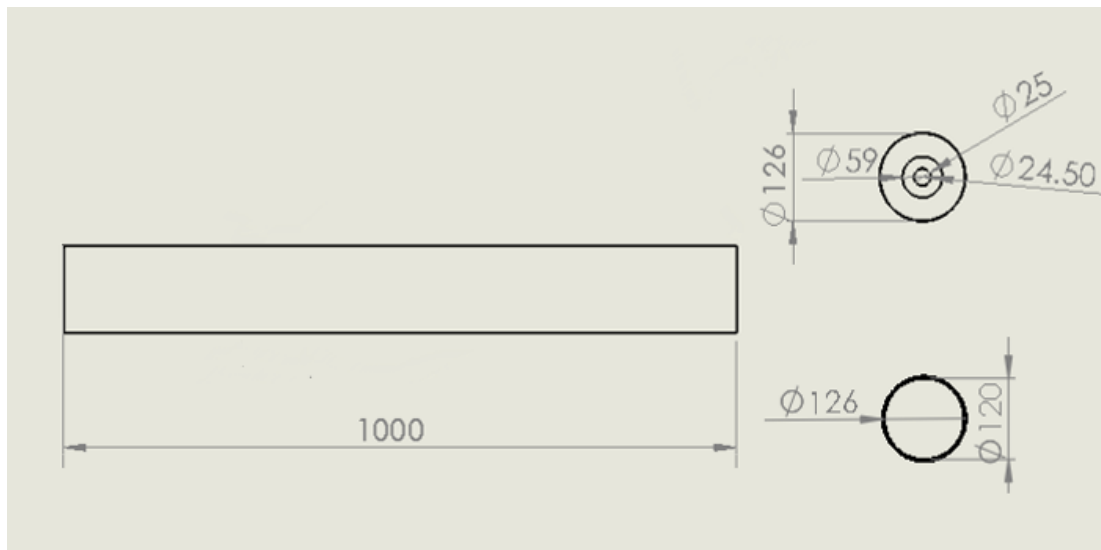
Perfil y dimensiones de la CC con acotaciones en mm.
